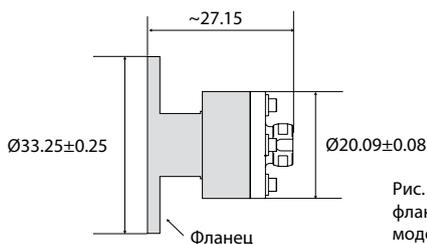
Габаритные размеры фланца коллиматора лазеров моделей FFS100CH1/200 для диаметра пучка 2.1/2.0 мм.
